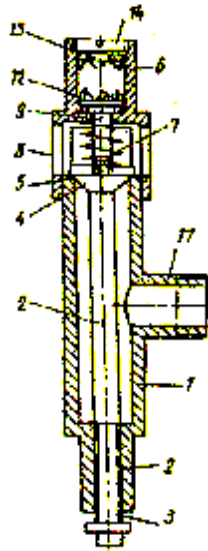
Устройство для комбинированного микроорошения: 1 – корпус; 2 – шток; 3 – спиральный канал; 4 – конусный клапан; 5 – седло; 6 – корпус механизма фиксации; 7 – пружина; 8 – окно; 9 – стержень; 10 – диск; 11 – зубчатый венец; 12 – пазы; 13 – диск; 14 крышка; 15 – направляющие выступы; 16 – эластичный клапан; 17 - патрубок
